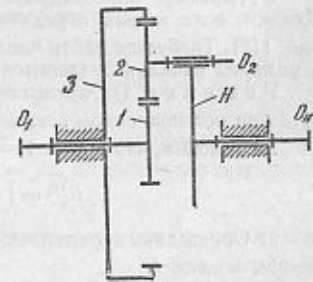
Схема одноступенчатого планетарного однорядного редуктора типа Джемса.
